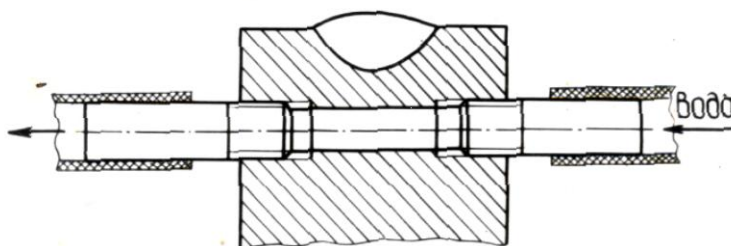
Схема охлаждения металла сварного соединения в процессе сварки.
